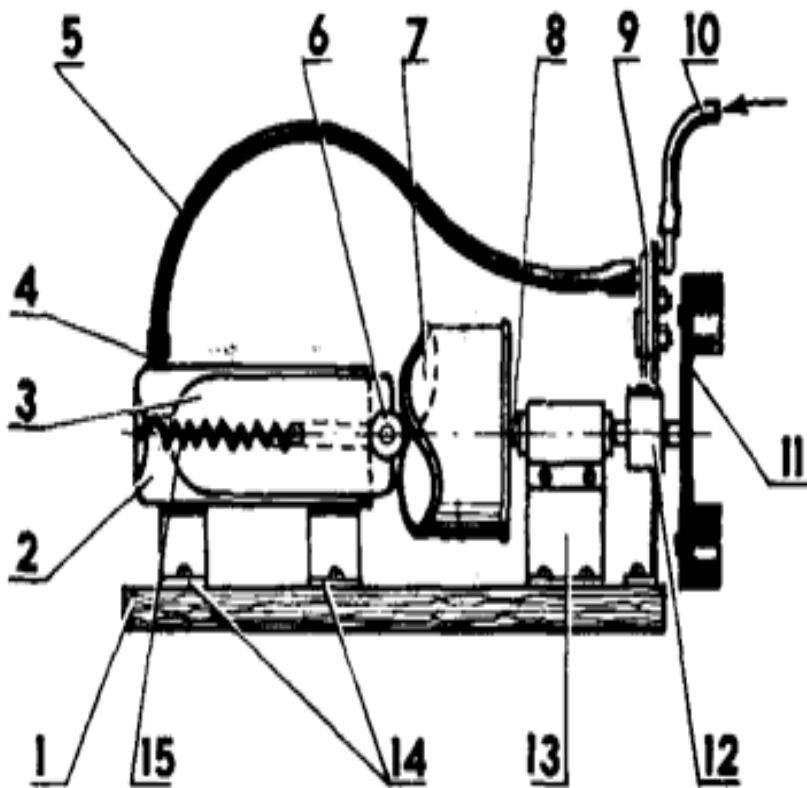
Механизм преобразования прямолинейного движения поршня во вращательное движение вала: 1 – основание, 2 - рабочий цилиндр, 3 - поршень, 4 - выпускной патрубок, 5 - шланг, 6 - ролик, 7 - цилиндрический кулачок, 8 - вал двигателя, 9 - золотник, 10 - патрубок подачи сжатого воздуха, 11 - маховик, 12 - кулачок привода золотника, 13 - кронштейн крепления вала, 14 - кронштейны крепления рабочего цилиндра, 15 - возвратная пружина
